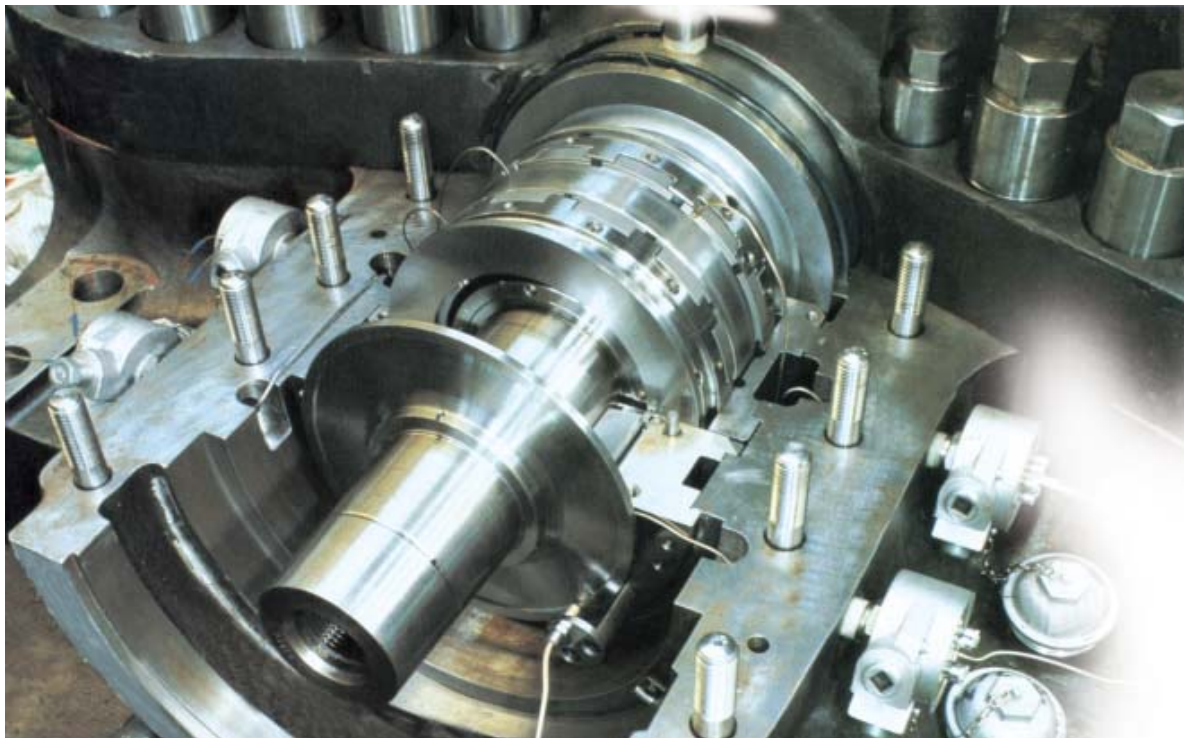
Vista del eje de un compresor. Fuente: Tomado de [2]
